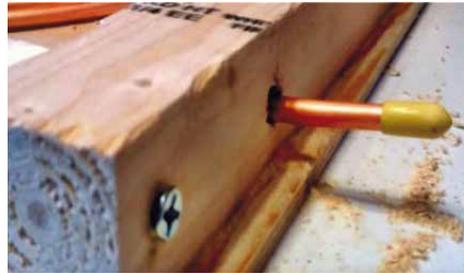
Сверлим отверстия в боковых брусках для вывода трубки
